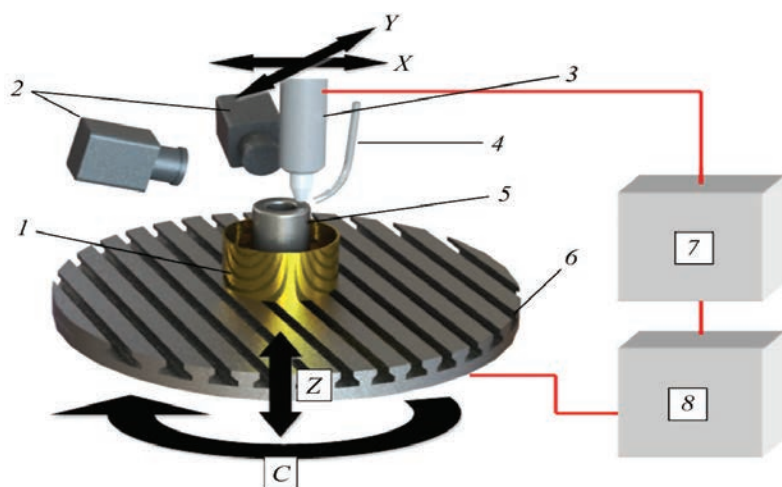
Схема установки для плазменно-дуговой трехмерной печати объемных изделий (обозначения см. в тексте)
